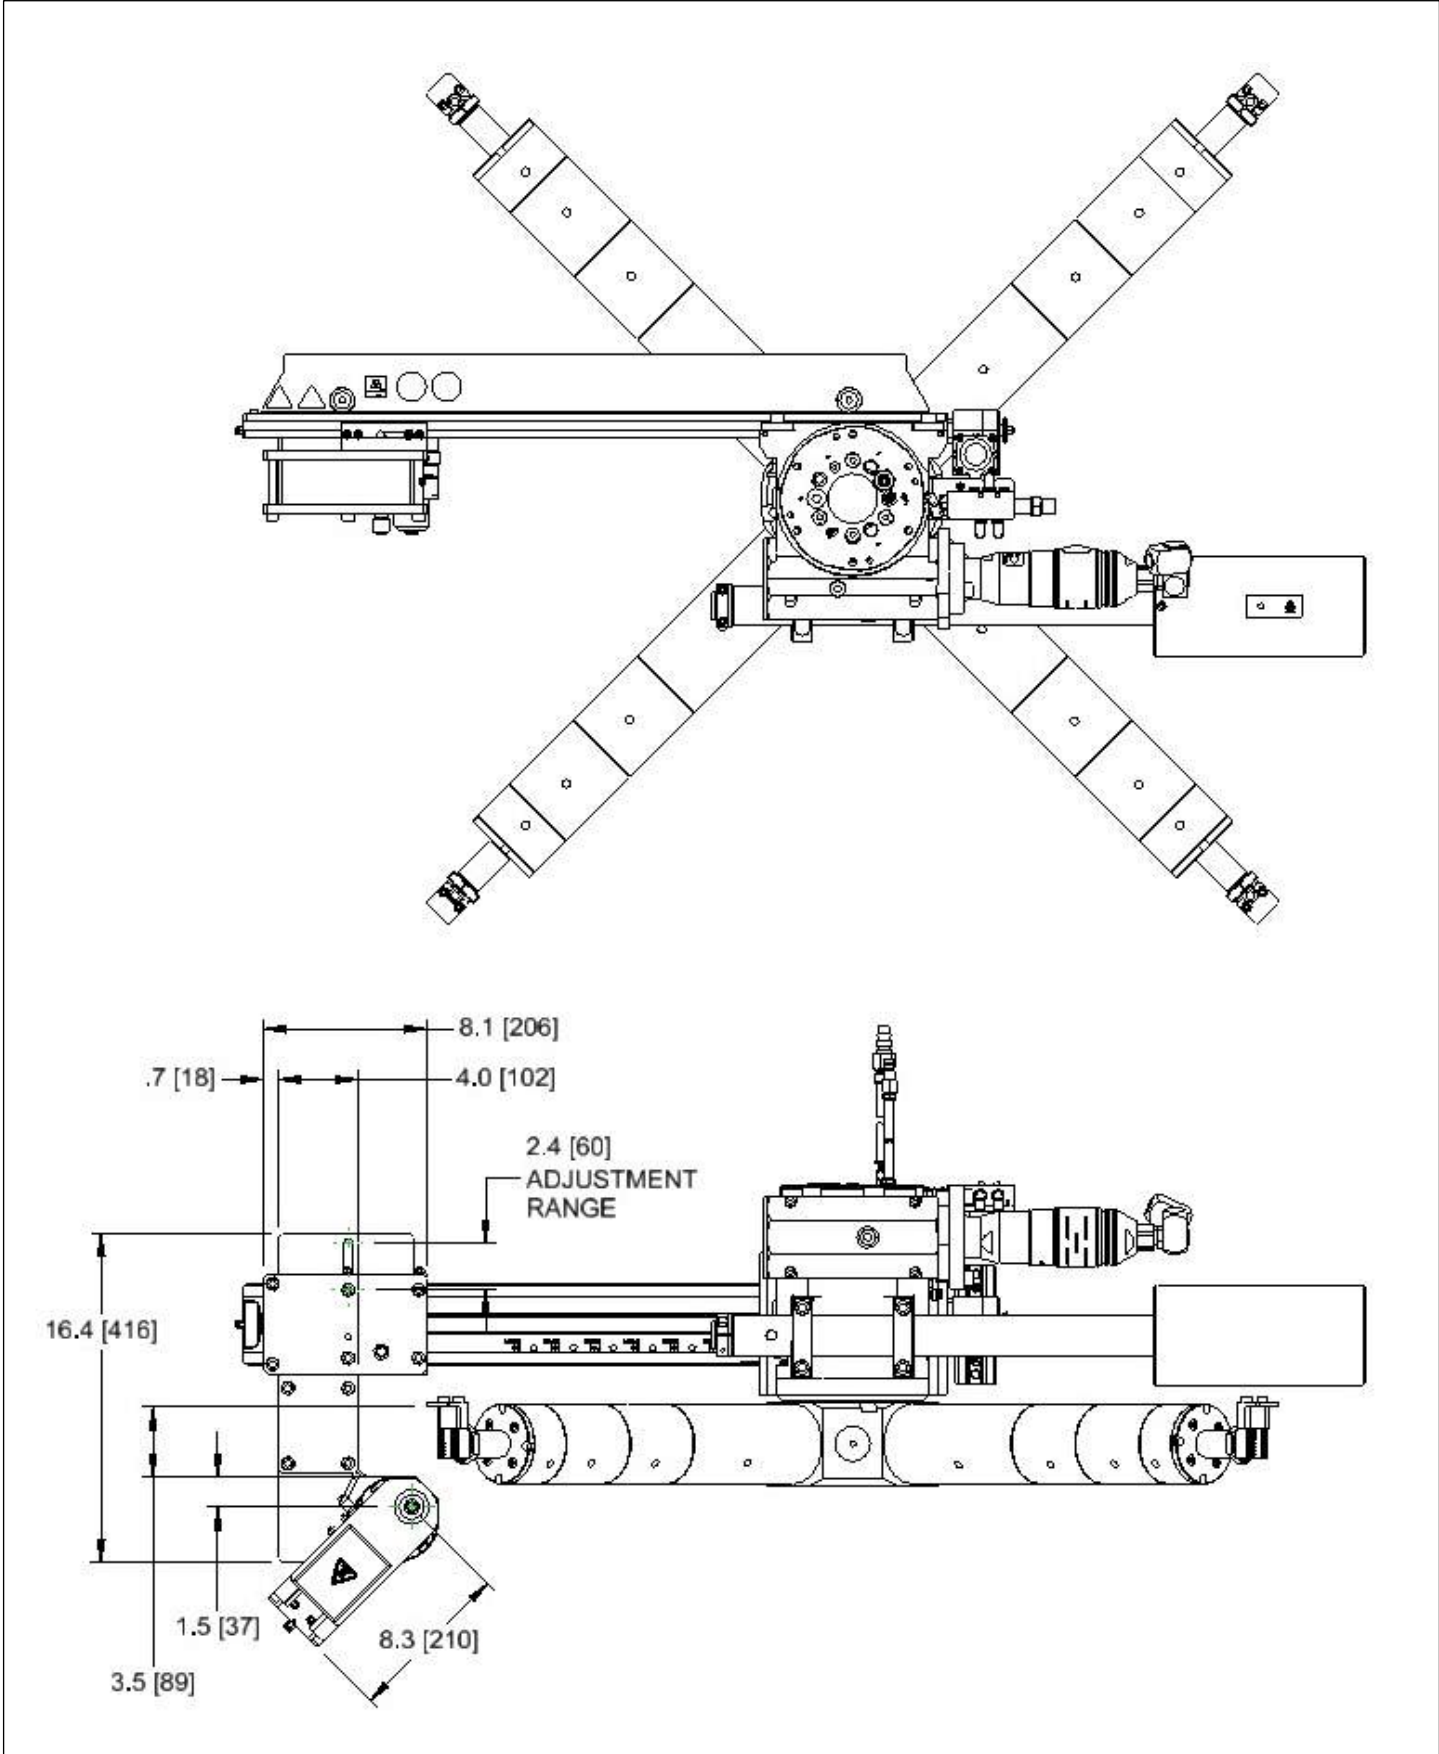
FF6300 Abmessungen der rückseitigen Anbringung
